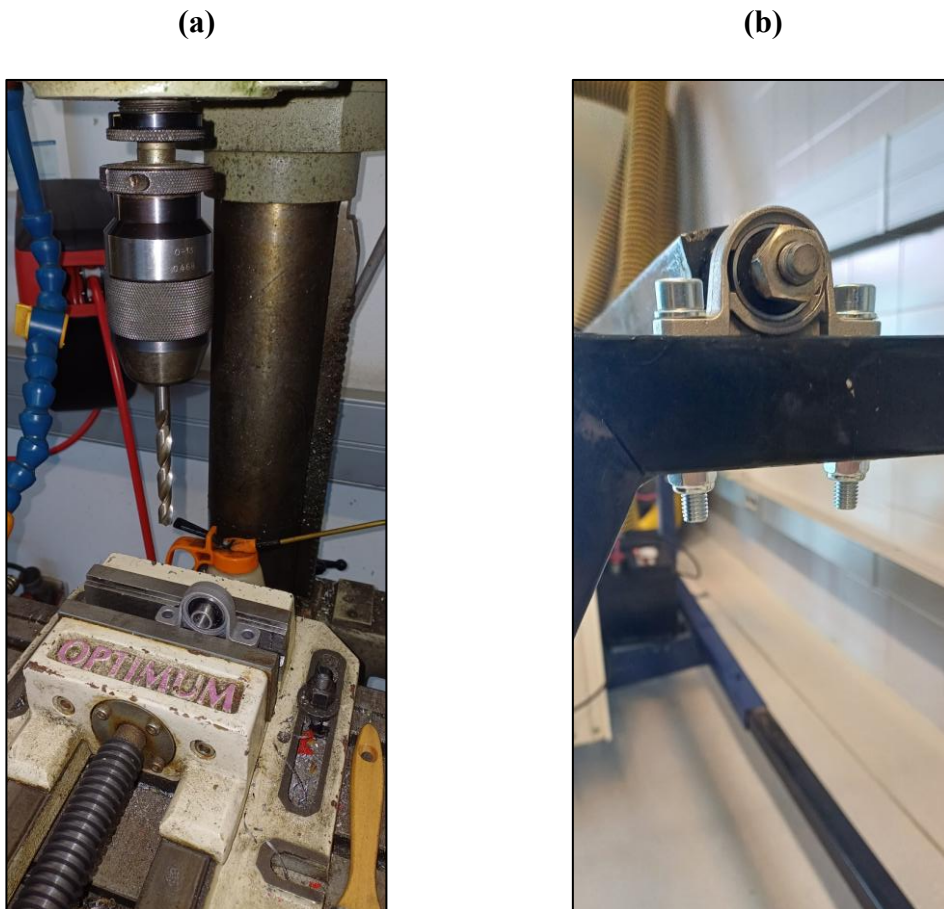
(a) Taladrado de rodamientos, (b) Resultado del montaje de rodamientos.
